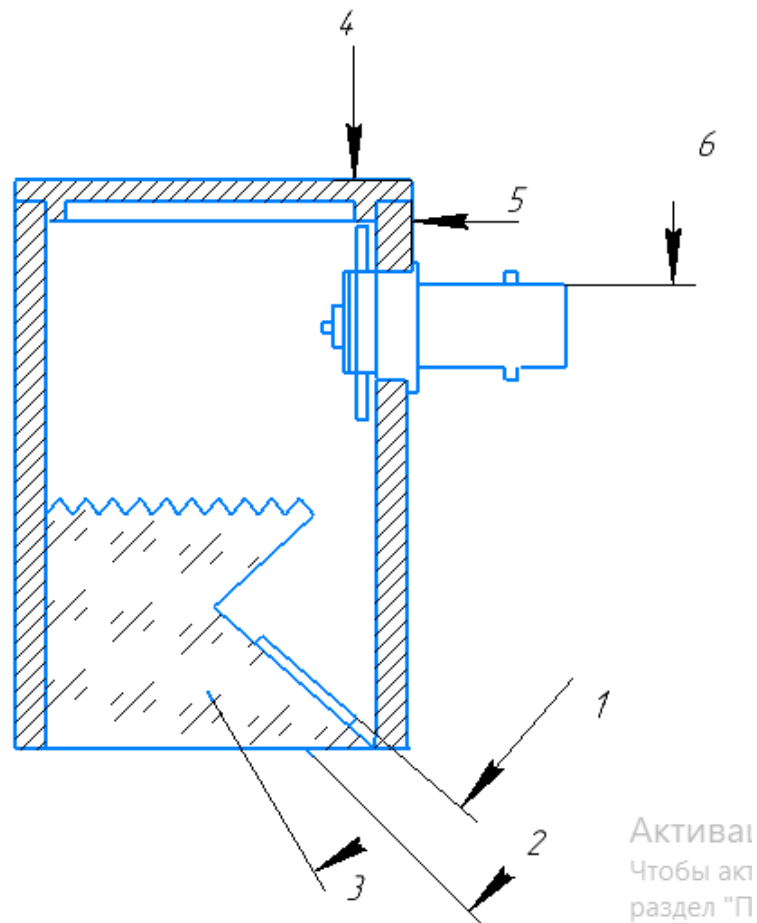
Конструкція перетворювача: 1 - п'єзоелемент; 2 – протектор; 3 – призма; 4 – кришка; 5 – корпус; 6 - роз'єм BNC
